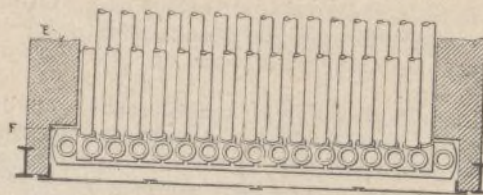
Alzada posterior y plano parcial de una caldera provista de tubos compensadores para facilitar la circulación.
